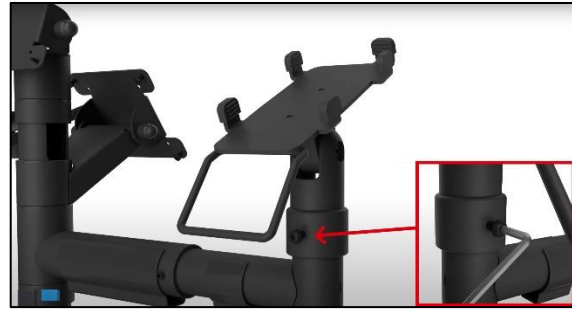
EFT auf Arm mit Winkelanschlag.
